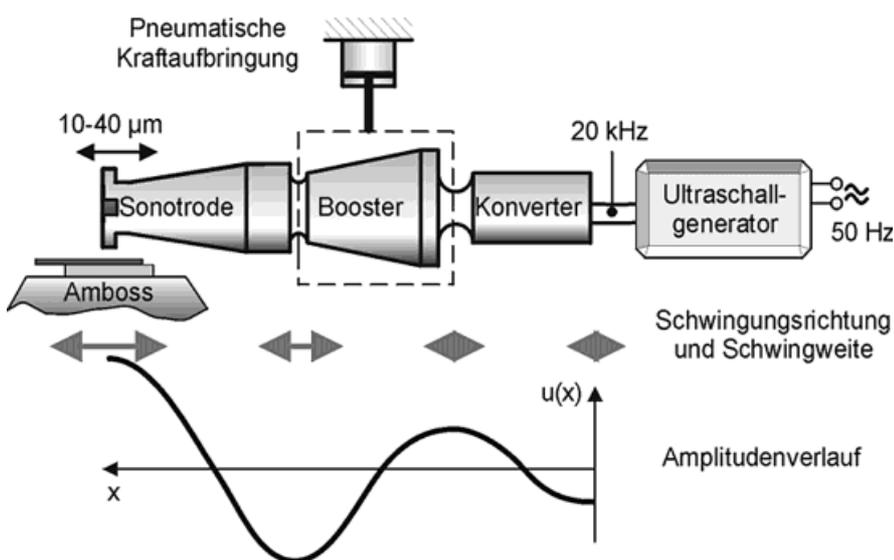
Prinzip des Ultraschallschweißens
